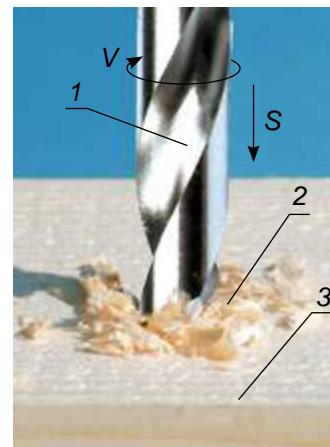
Образование стружки при сверлении: 1 – сверло; 2 – стружка; 3 – заготовка
